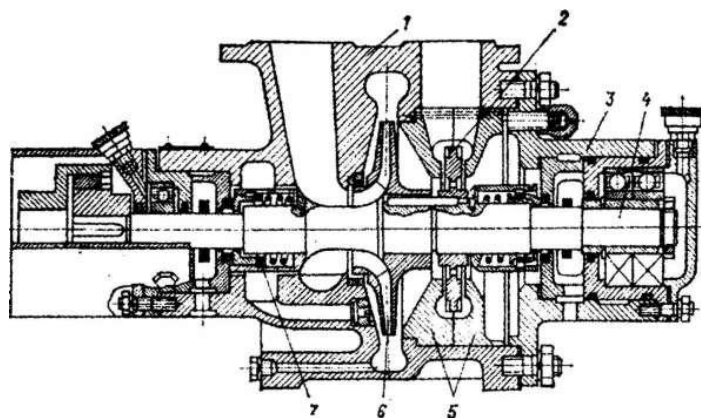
Центробежно-вихревой насос: 1 - корпус; 2 - вихревая ступень; 3 - крышка; 4 - вал; 5 - неподвижные вставки; 6 - центробежная ступень; 7 - торцевое уплотнение
